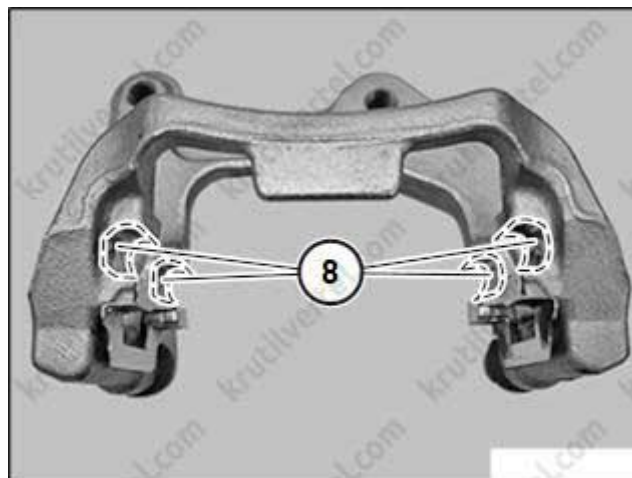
Очистка контактної поверхні направляючих:
